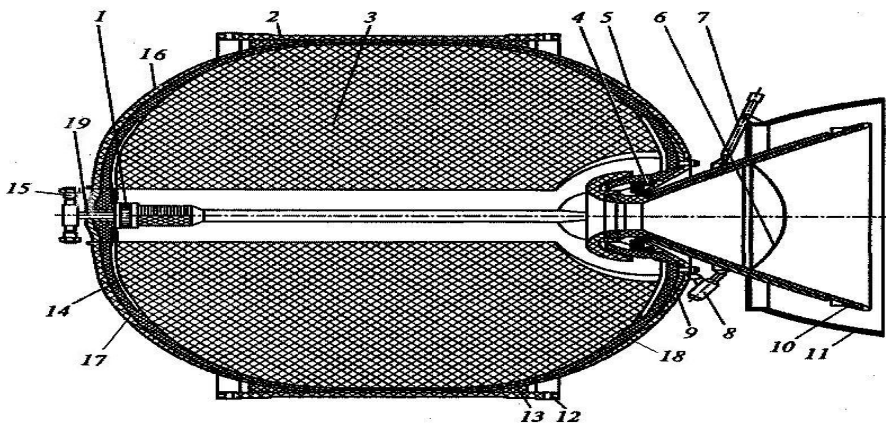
Схема РДТТ [3]: 1 – воспламенитель; 2 – обечайка типа «кокон»; 3 – заряд твердого топлива; 4 – опорный шарнир; 5, 16 – заднее и переднее днище; 6 – сопловая заглушка; 7 – механизм раздвижки сопла; 8 – рулевая машинка; 9 – закладной фланец; 10 – сопловой блок; 11 – выдвижной насадок; 12 – стыковочный шпангоут; 13 – эластичный клин; 14 – раскрепощающая манжета; 15 – пиропатрон; 17 – защитно-крепящий слой; 18 – теплозащитное покрытие; 19 – направляющие воспламенительного устройства
